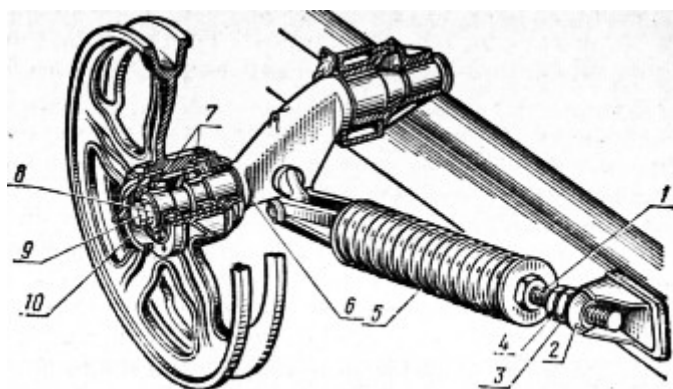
Направляющее колесо с натяжным амортизирующим устройством трактора ДТ-75: 1 — болт натяжной; 2 — опора шаровая; 3 — гайка регулировочная; 4 — контргайка; 5 — большая и малая цилиндрические пружины; 6 — коленчатая ось; 7 — конические роликоподшипники; 8 — гайка регулировочная; 9 — контргайка; 10 — крышка.
